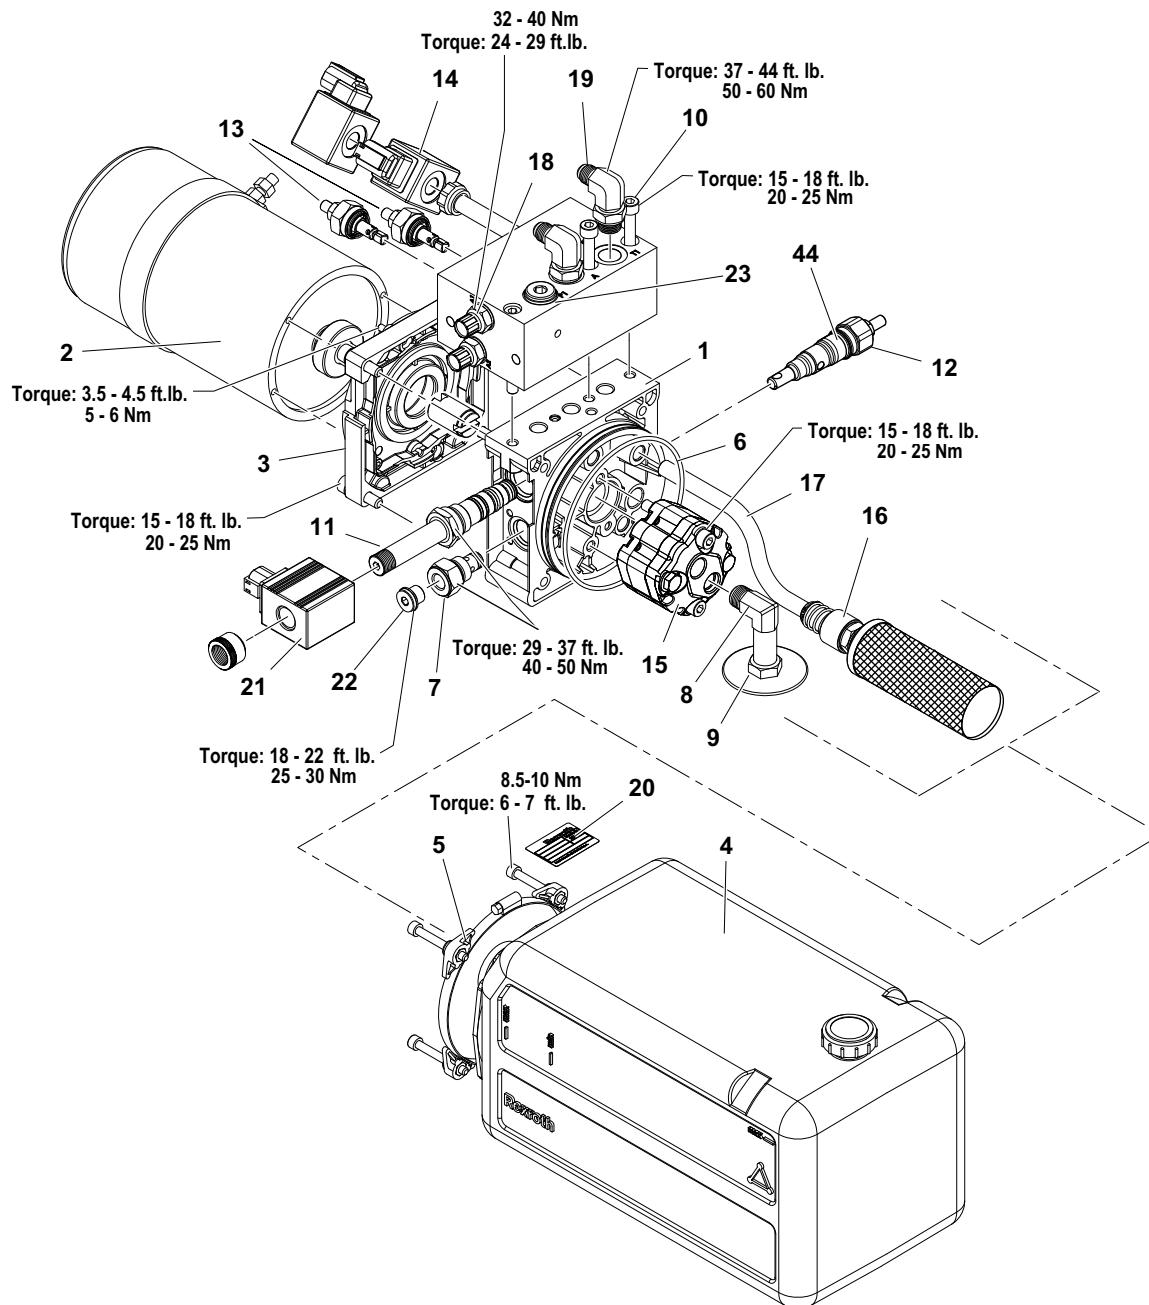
Motor hidráulico, conjunto da bomba e do tanque (todas as máquinas)
